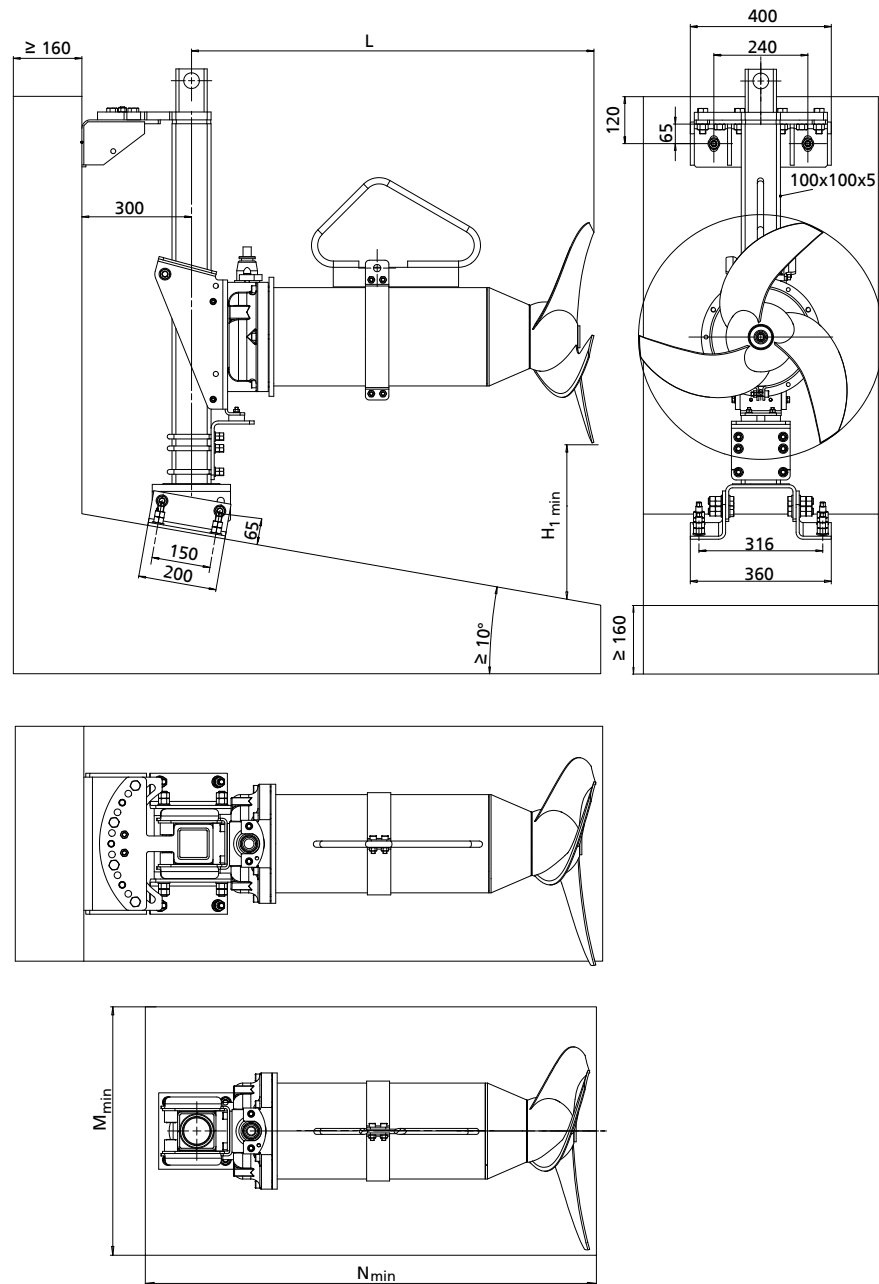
Установка принадлежностей 22 — Атаміх 400 (только типоразмер 4135) / 600
